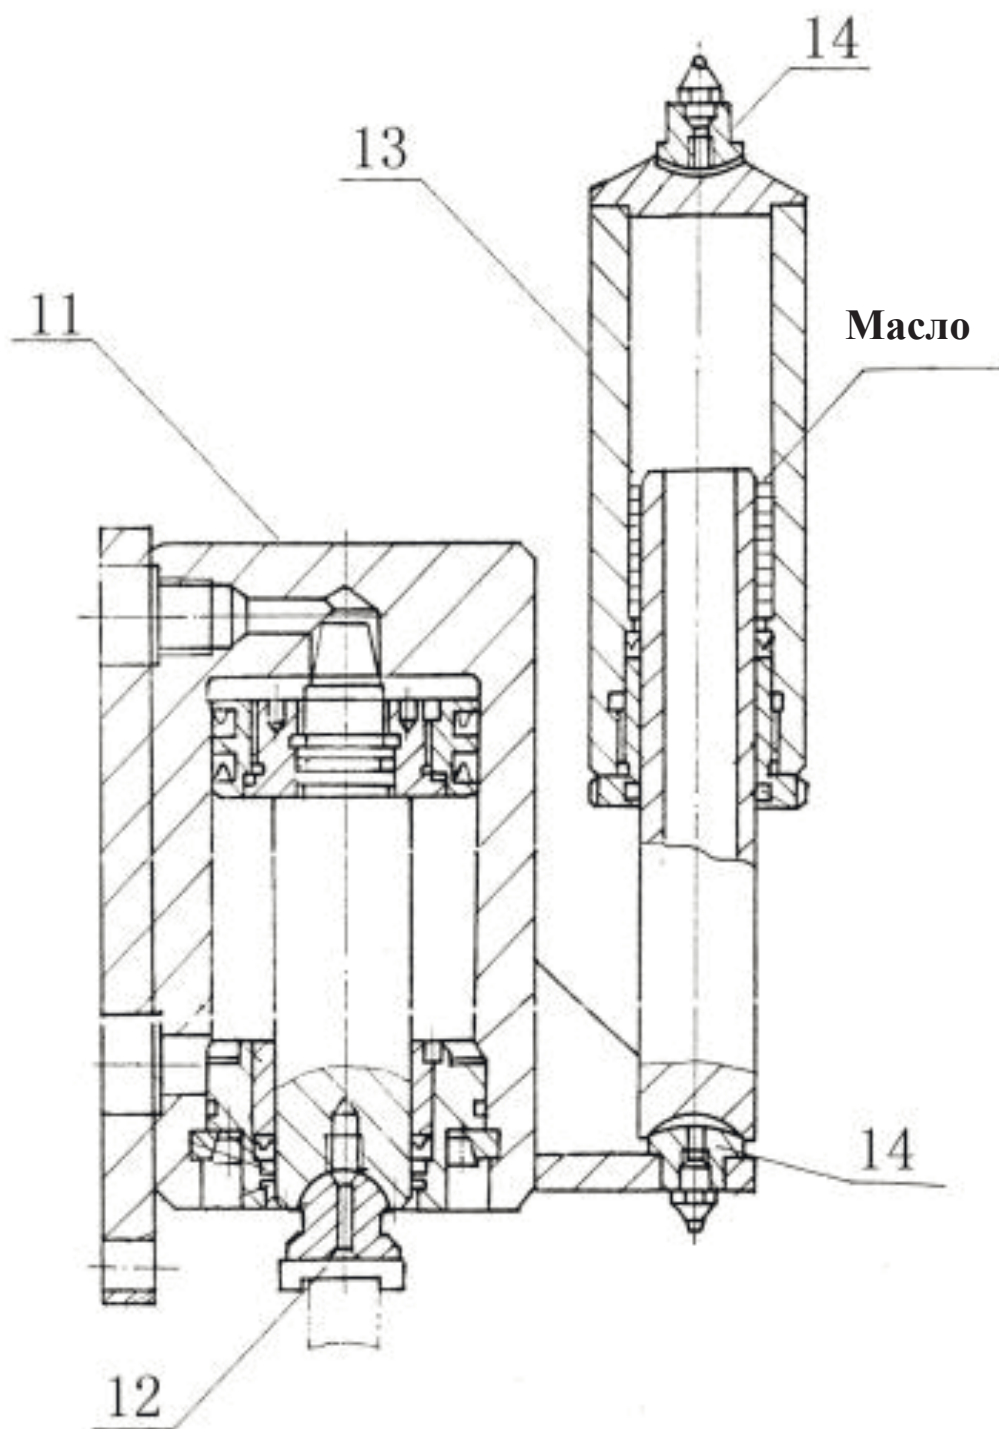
Левый гидравлический цилиндр и цилиндр обратного хода
